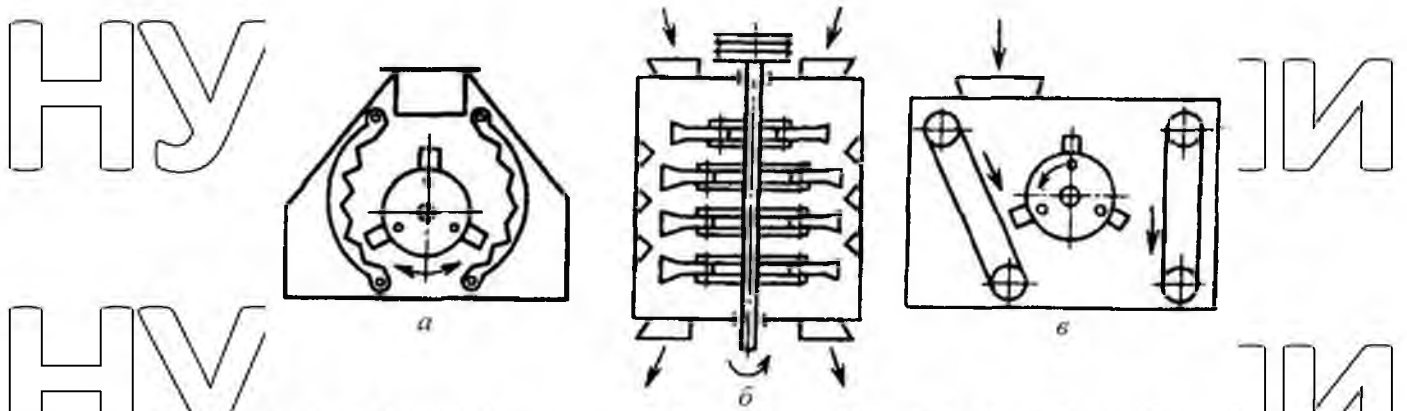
Схеми конструкцій дробарок [24, с. 226]: а – реверсна; б – з вертикально розміщеним валом; в – з полотном для очищення
